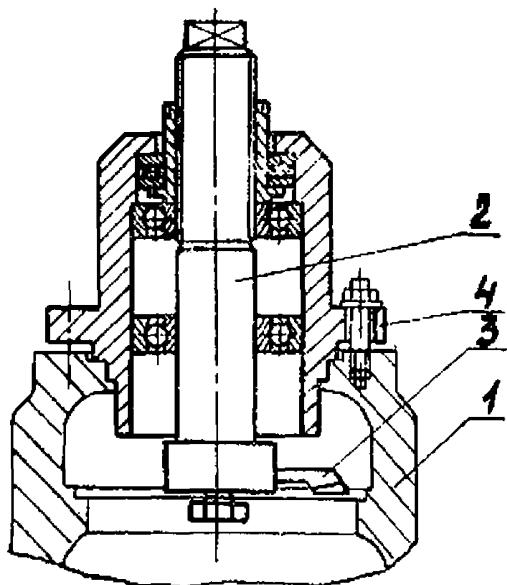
Приспособление для расточки поверхности под седла клапанов насоса ПДГ:
